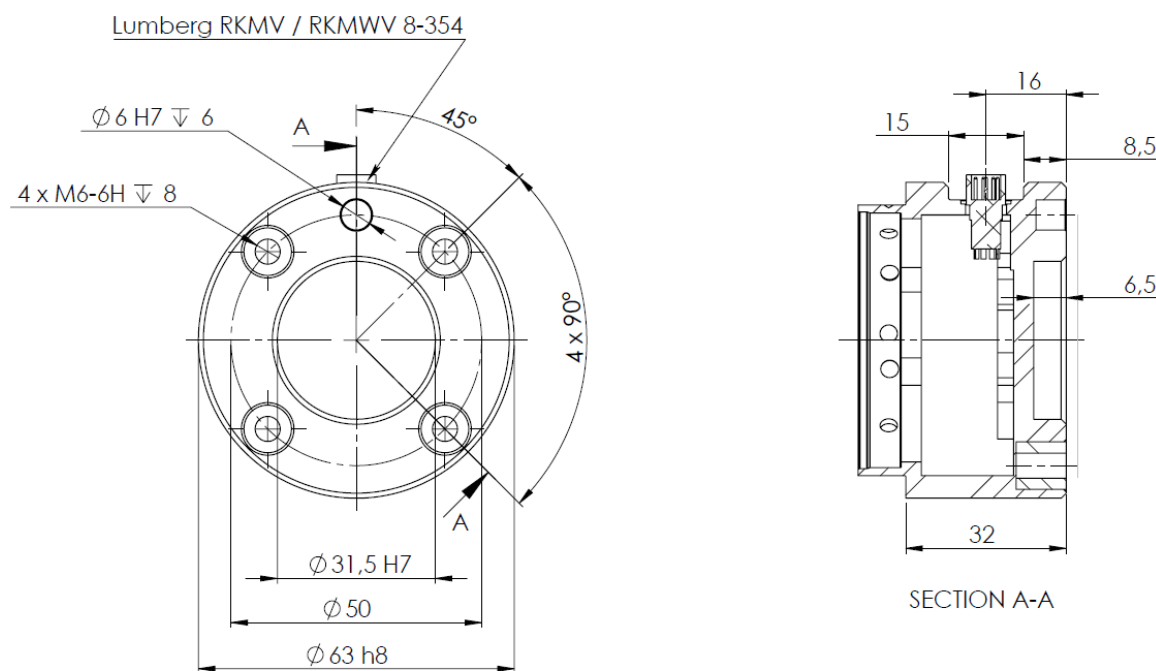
La flangia di uscita dell'utensile, ISO 9409-1-50-4-M6. Qui viene montato l'utensile alla sommità del robot. Tutte le misure sono in mm.
